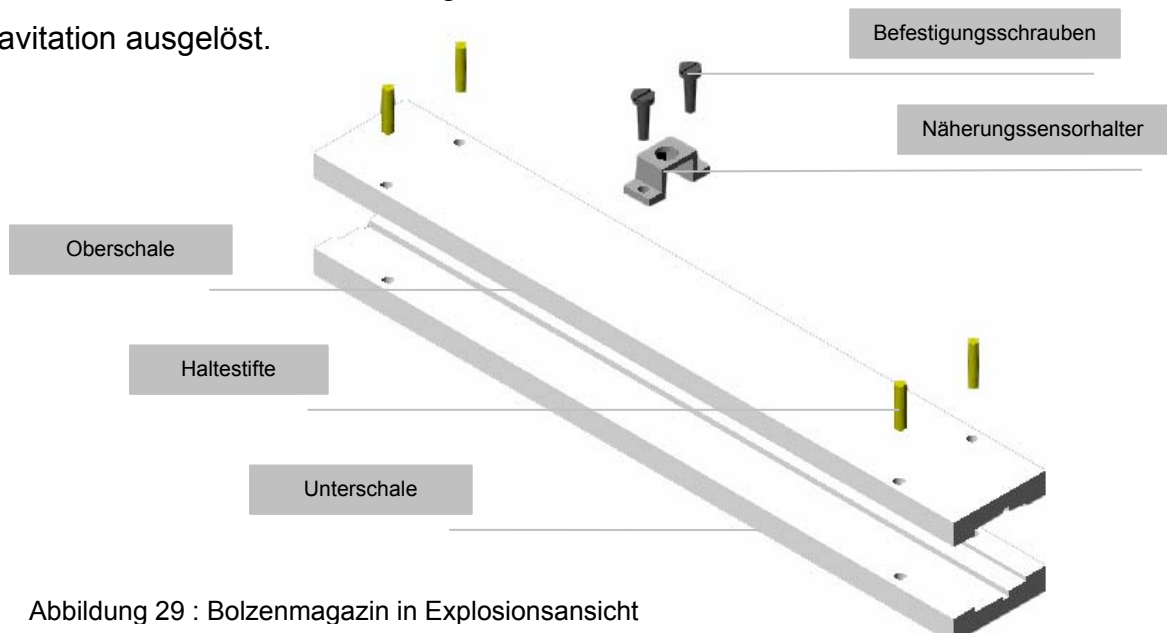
Bolzenmagazin in Explosionsansicht
